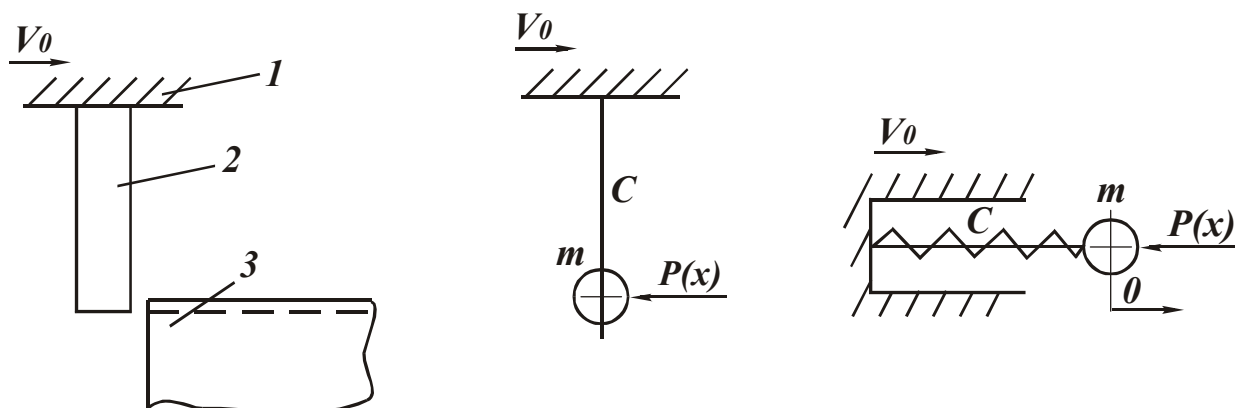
Расчетные схемы взаимодействия инструмента с деталью: 1 – привод станка, 2 – режущий инструмент, 3 – деталь.
